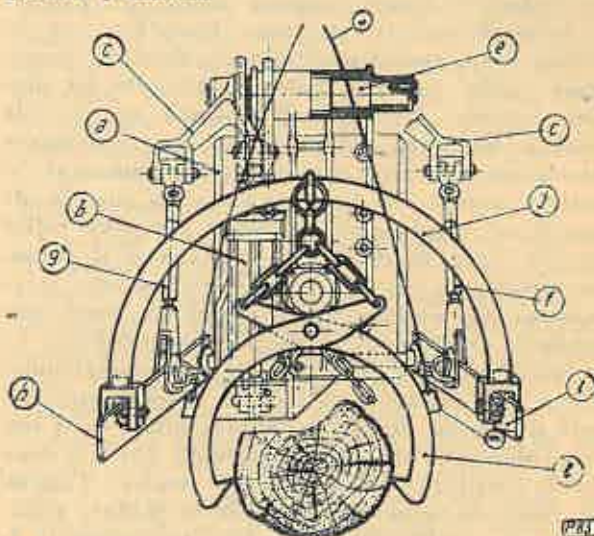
Dispozitiv de ridicare hidraulic cu clește: a — suport; b — cilindrul de forță; c, d — pîrghii; e — ax turnant; f, g — tiranți verticali; h, i — tiranți longitudinali; I — suport; I — clește; m — brățară; n — cablu de manevrare.
